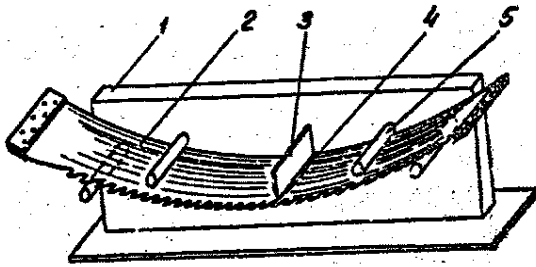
Приспособление для проверки степени вальцевания рамных пил: 1 - основание; 2 - пила; 3 - поверочная линейка; 4 - световая щель; 5 – упоры.
